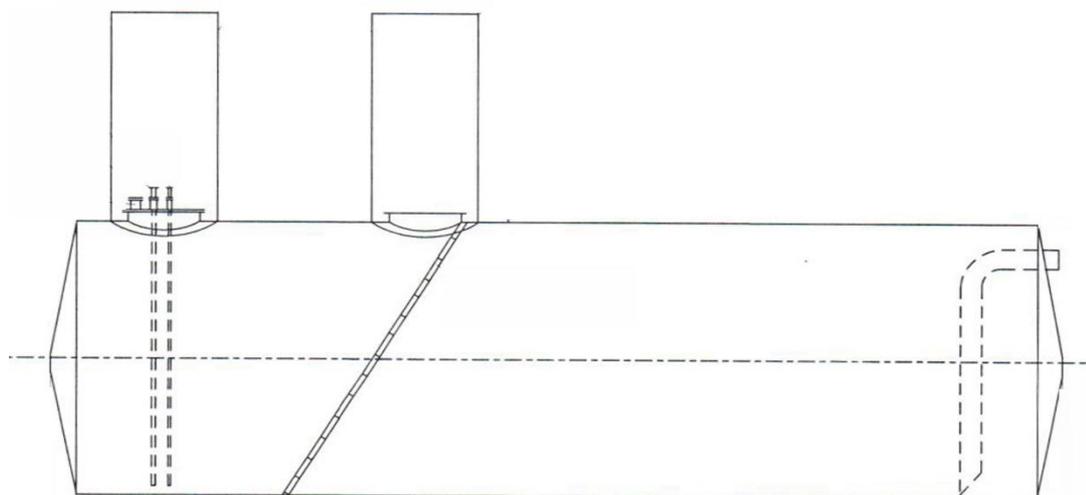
Эскиз подземного резервуара РГСП-50 № 468
